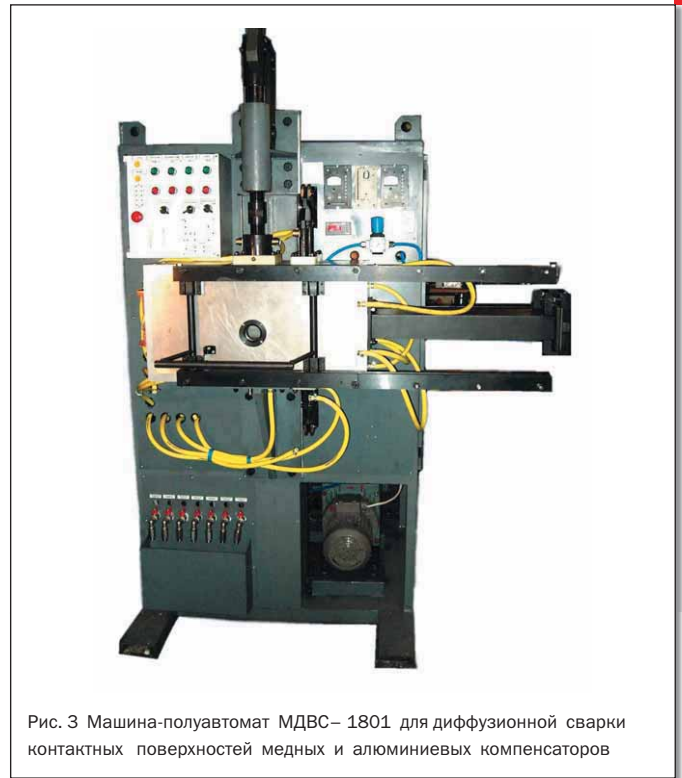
Машина-полуавтомат МДВС– 1801 для диффузионной сварки контактных поверхностей медных и алюминиевых компенсаторов
